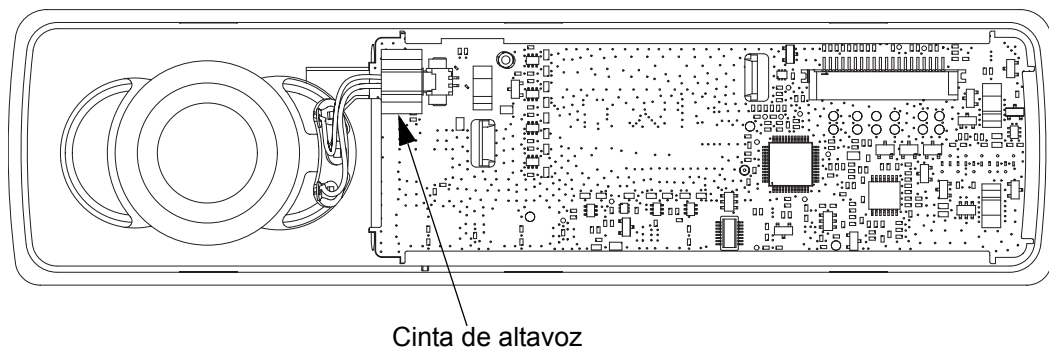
Montaje de la cinta del altavoz en la PCB
